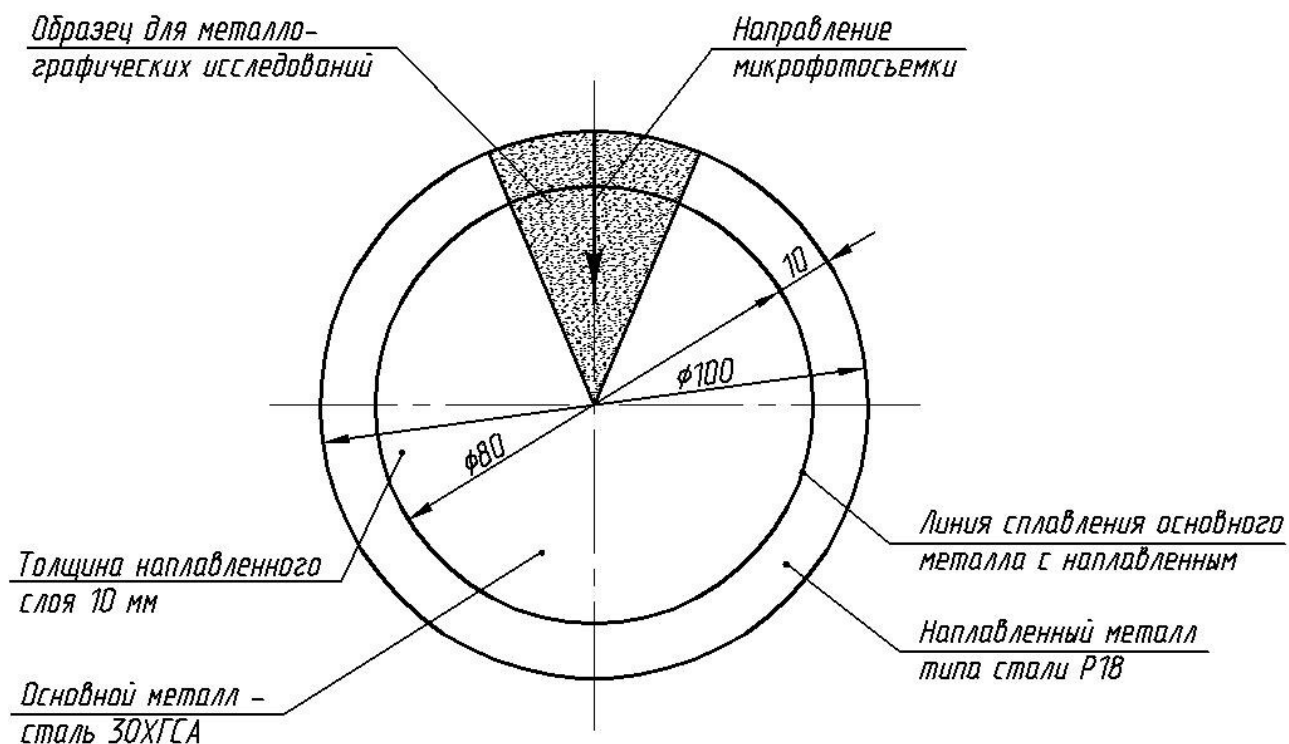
Схема вырезки образцов из наплавленного металла
